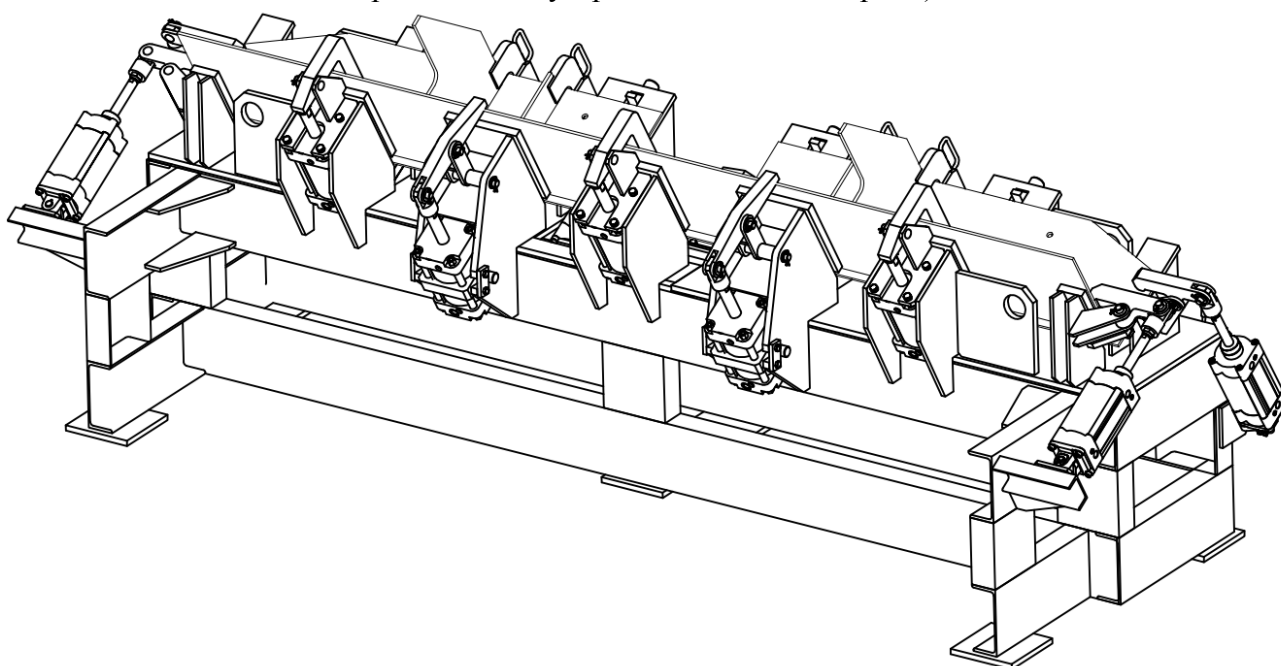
Модель станда сборки балки концевой (оснащен пневматическими прижимными устройствами. Вид сзади)
